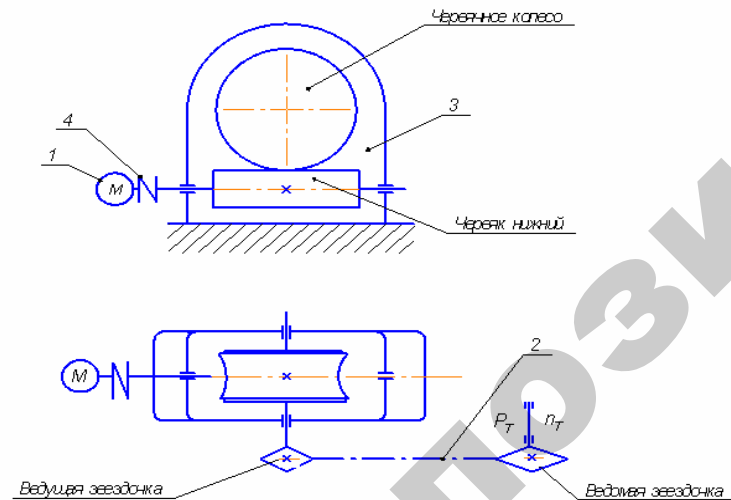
Кинематическая схема привода с червячным редуктором и цепной передачей
